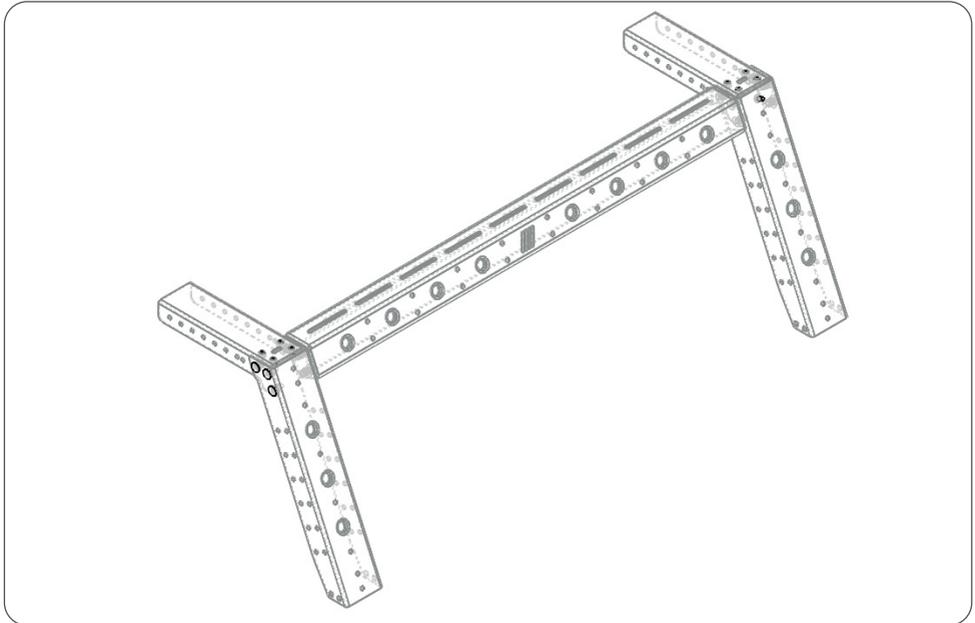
komplett verschraubte Eckstrebe / completely bolted corner strut
